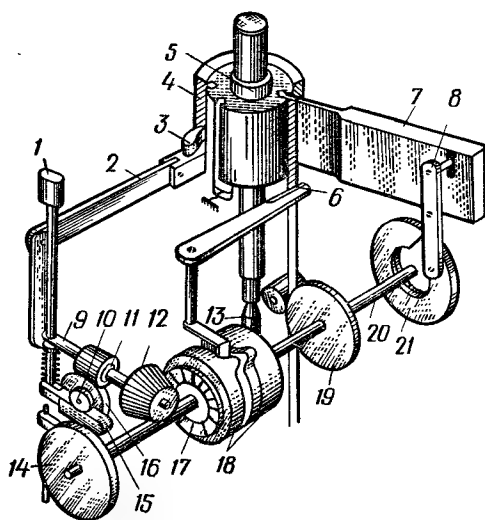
Кинематическая схема станка для изолировки пазов якорей
